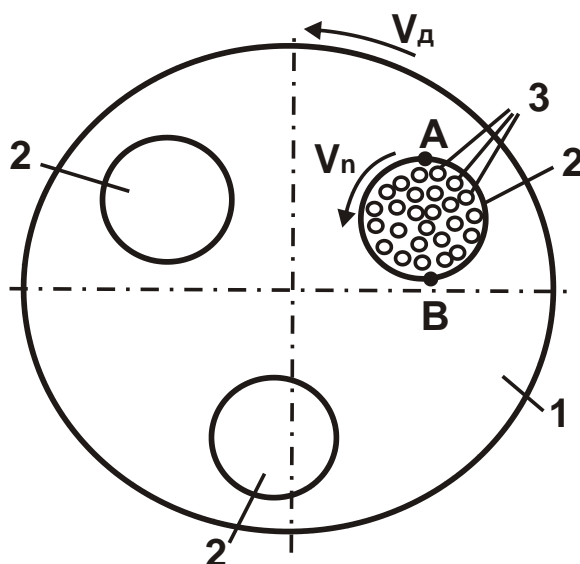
Кінематична схема доведення торцевих поверхонь кілець: 1 – доводочного диск; 2 – притискачі; 3 – оброблювальні кільця;
